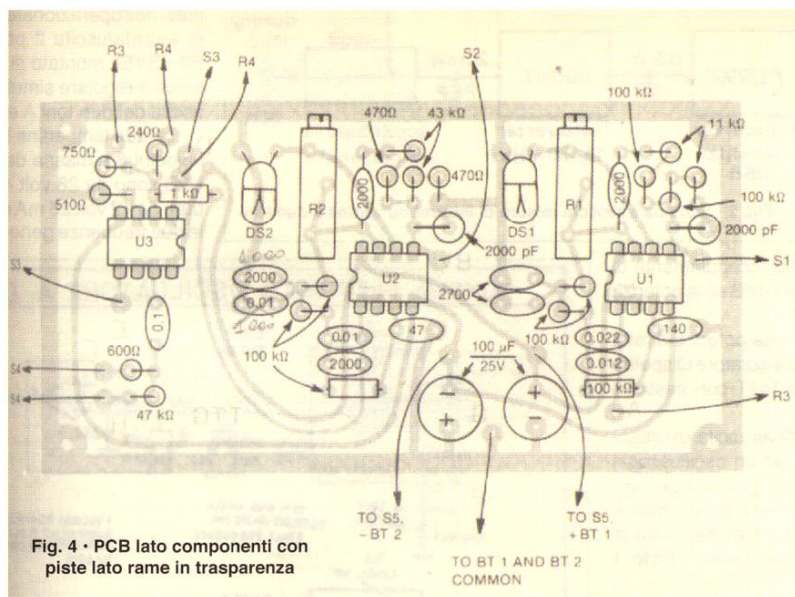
PCB lato componenti con piste lato rame in trasparenza
